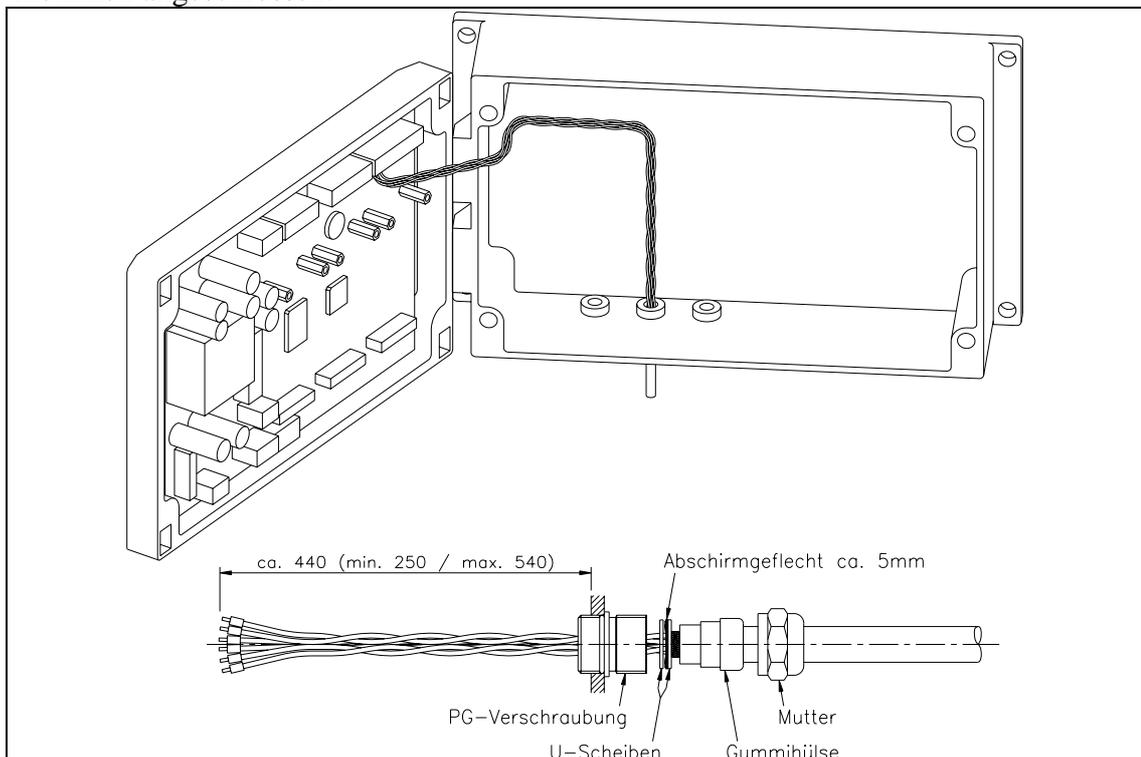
Verlauf der Anschlusskabel im Gehäuse
